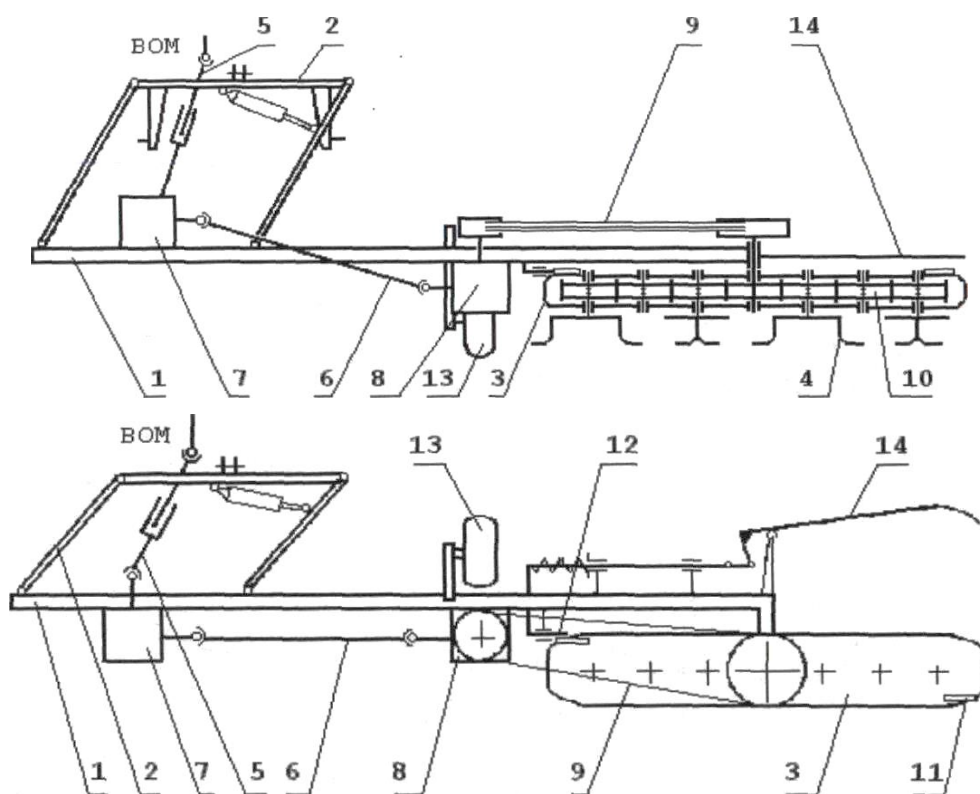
Схема четырехроторного вертикального фрезерного агрегата
